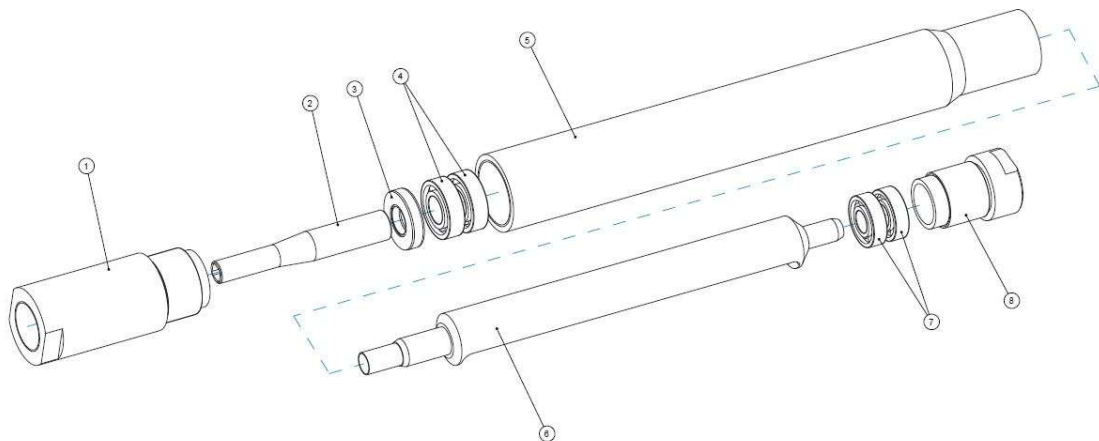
Explosionszeichnung des neu konstruierten Werkzeugträgers
